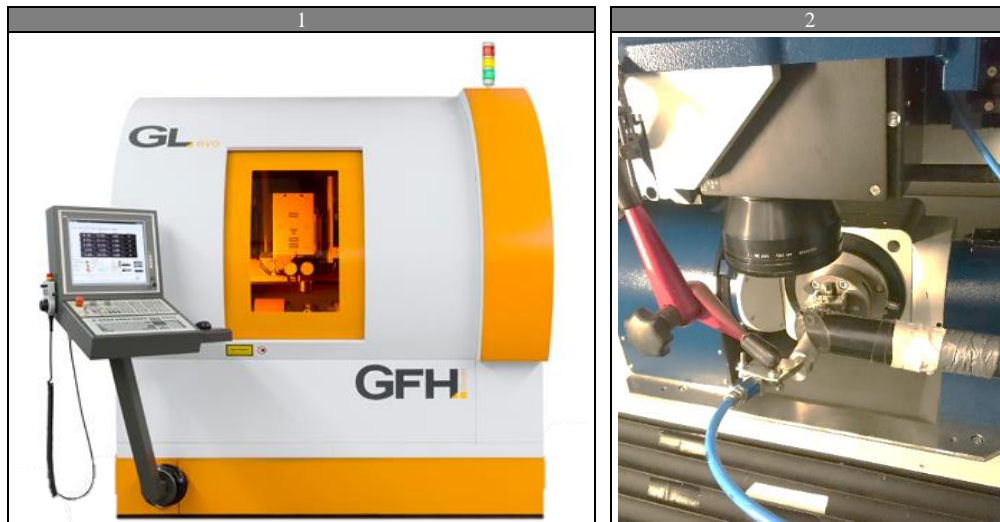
Machine-outil GFH (1), prise pièce (2)
